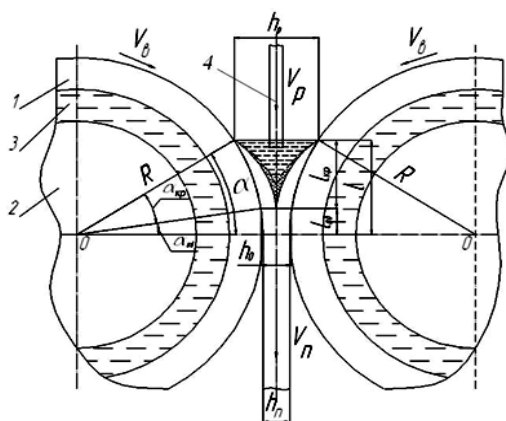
Схема процесса валковой разливки-прокатки в двухвалковом кристаллизаторе:
